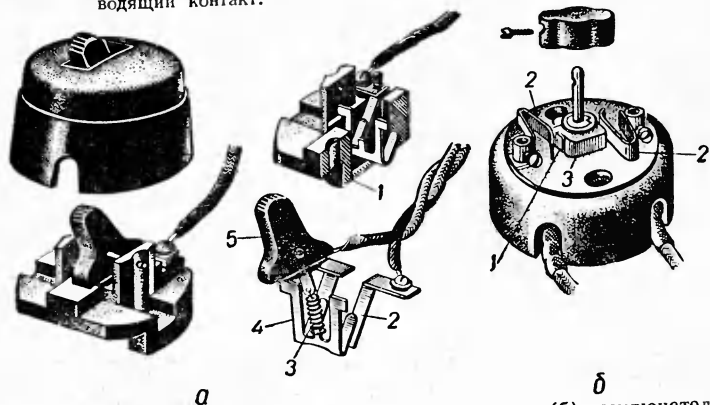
Устройство перекидного (а) и поворотного (б) выключателей.
